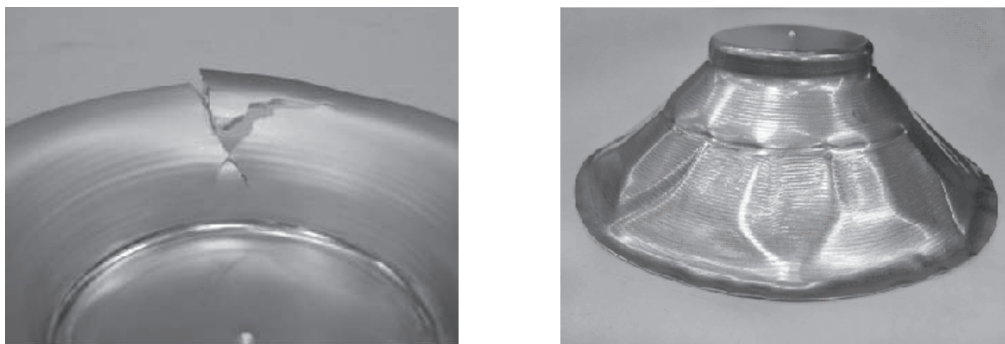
a) Bauteil mit radialem Riss b) Bauteil mit starker Faltenbildung
